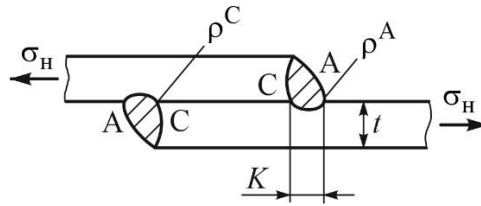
Сварные нахлесточные соединения с угловыми швами
